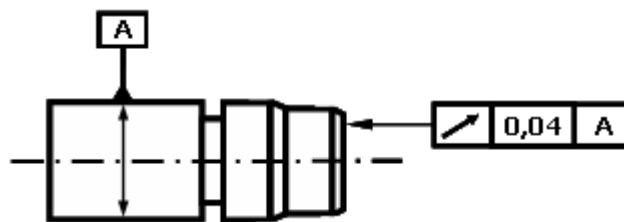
Indicação de tolerância de batida axial em desenho técnico
